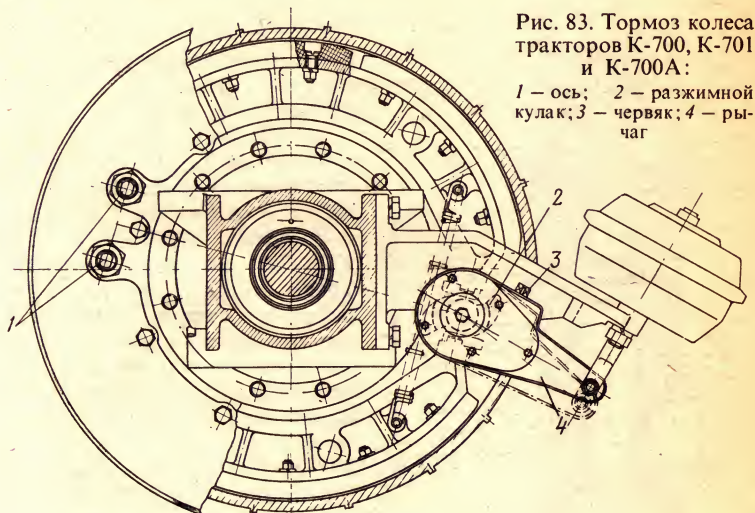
Тормоз колеса тракторов К-700, К-701 и К-700А:
